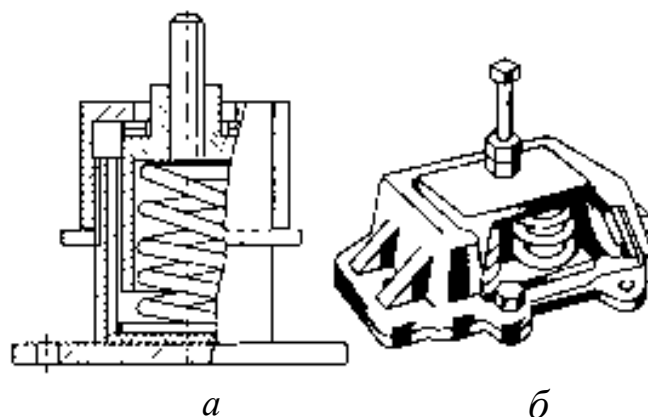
Пружинный и комбинированный виброизоляторы: а - цилиндрический пружинный амортизатор; б - пружинно-резиновый амортизатор
